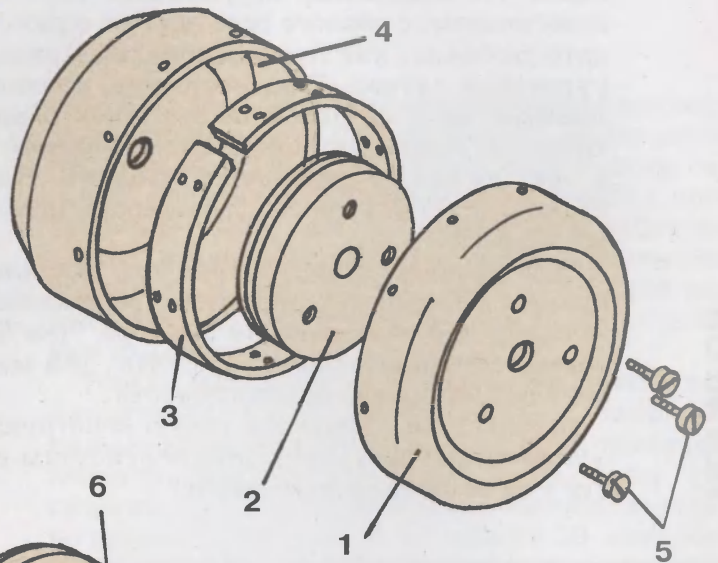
Детали колеса: 1 — половина колеса с крепежными отверстиями для большого шкива; 2 — большой шкив; 3 — соединительное кольцо; 4 — вторая половина колеса; 5 — винты крепления шкива.
